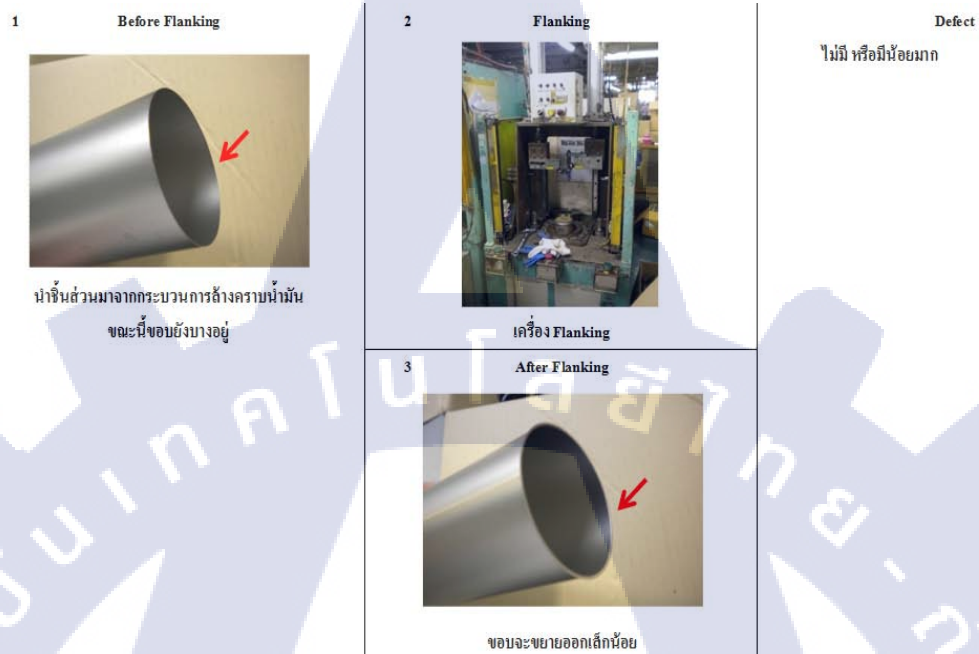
แสดงกระบวนการทำงานของแผนก Welding
